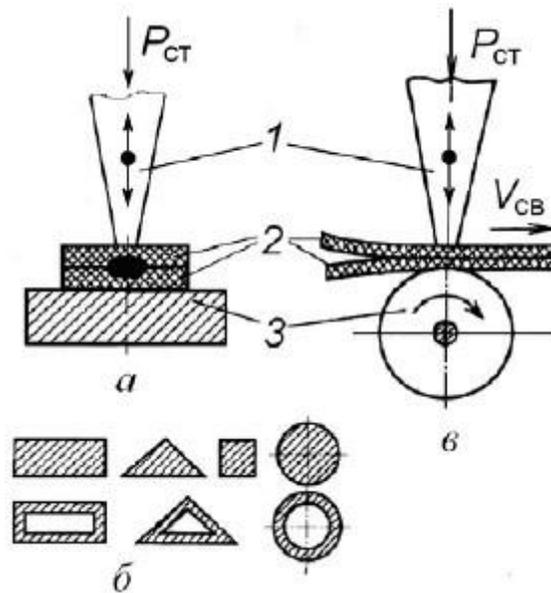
Схемы контактной ультразвуковой сварки: а – прессовая; б – возможная форма рабочего торца волновода при прессовой сварке; в – шовная; 1 – волновод; 2 – свариваемые детали; 3 – опора
